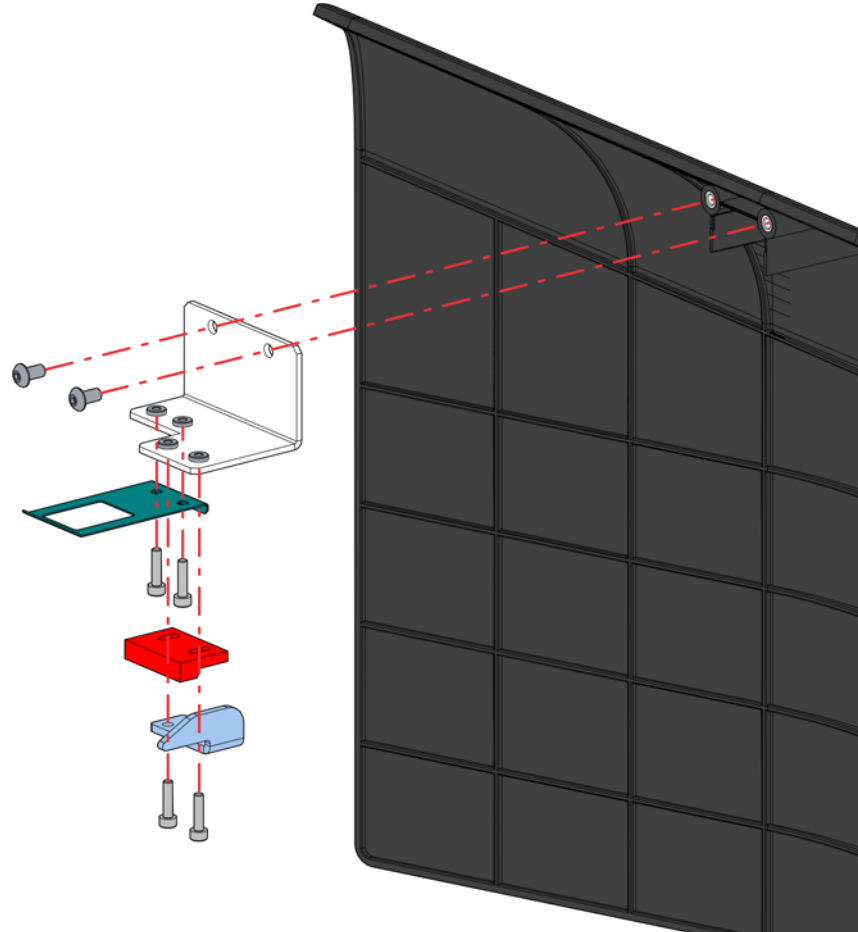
Positionen der Befestigungsschrauben für den Sensor der oberen Abdeckung](#)
